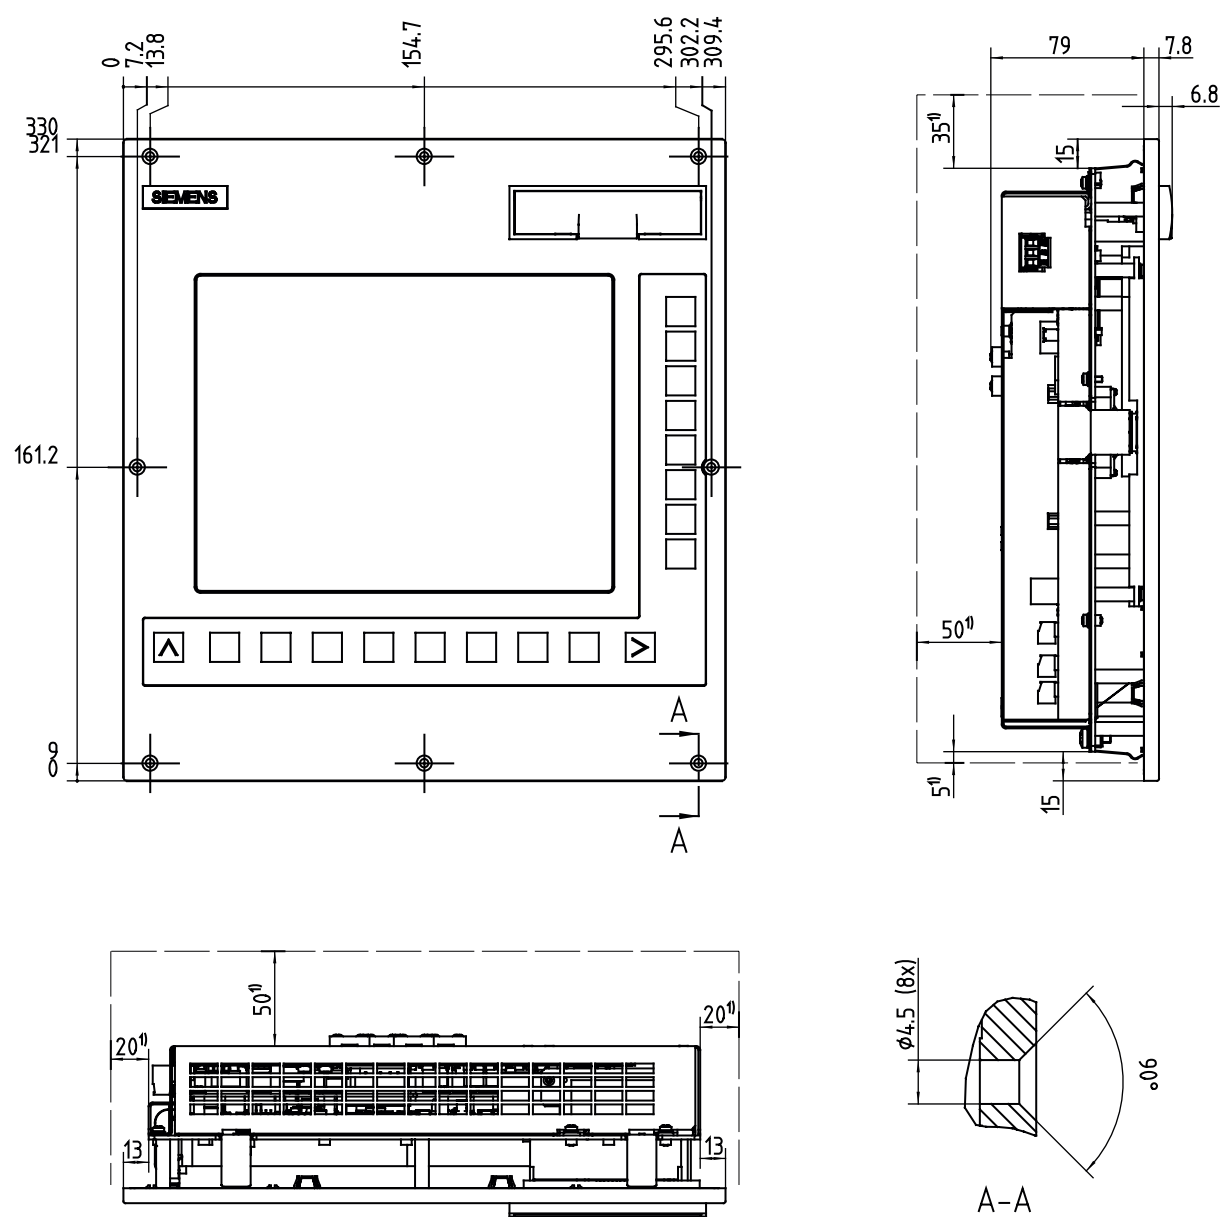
CNC 操作面板外形尺寸图 (PCU)
